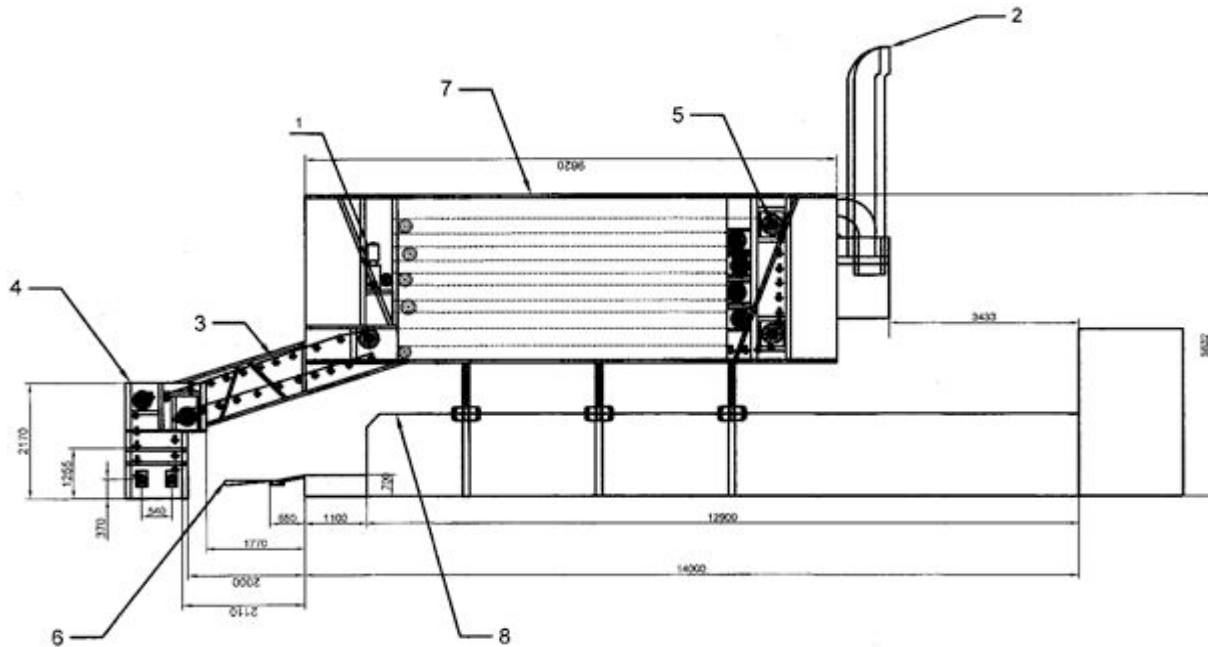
Колисковий кулер для охолодження: 1 – вентилятор; 2 – витяжна система; 3 – колиска; 4 – завантажувально-розвантажувальний транспортер; 5 – привідний вал; 6 – перевантажувальний транспортер; 7 – камера охолодження; 8 – тунельна піч; 9 – натяжний вал.
